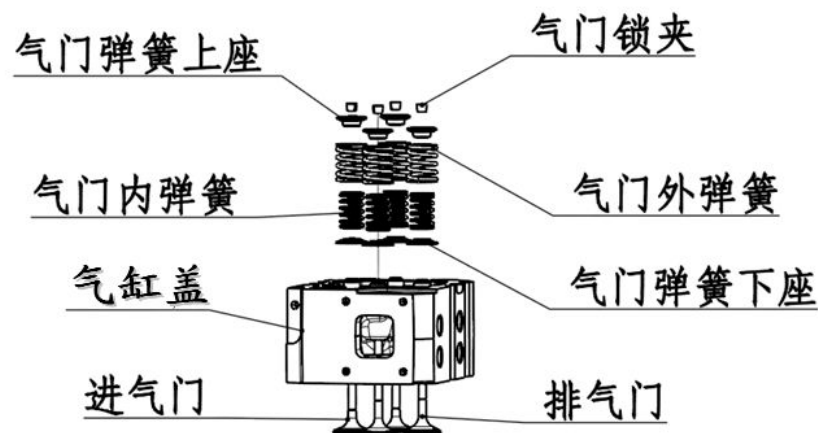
Группа клапанов дизельного двигателя карьерного самосвала 16M33
